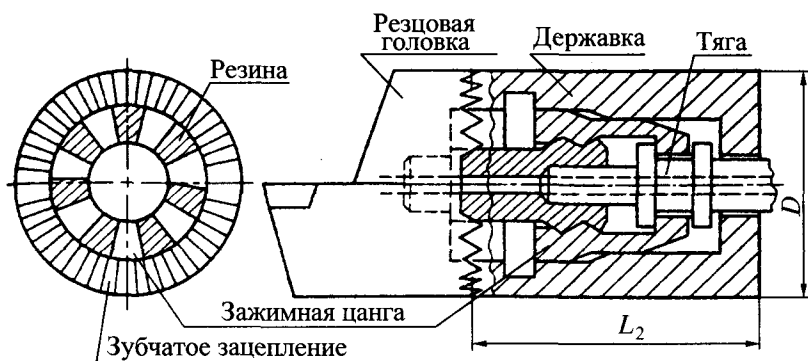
Конструкция узла крепления инструментальной системы FTS
